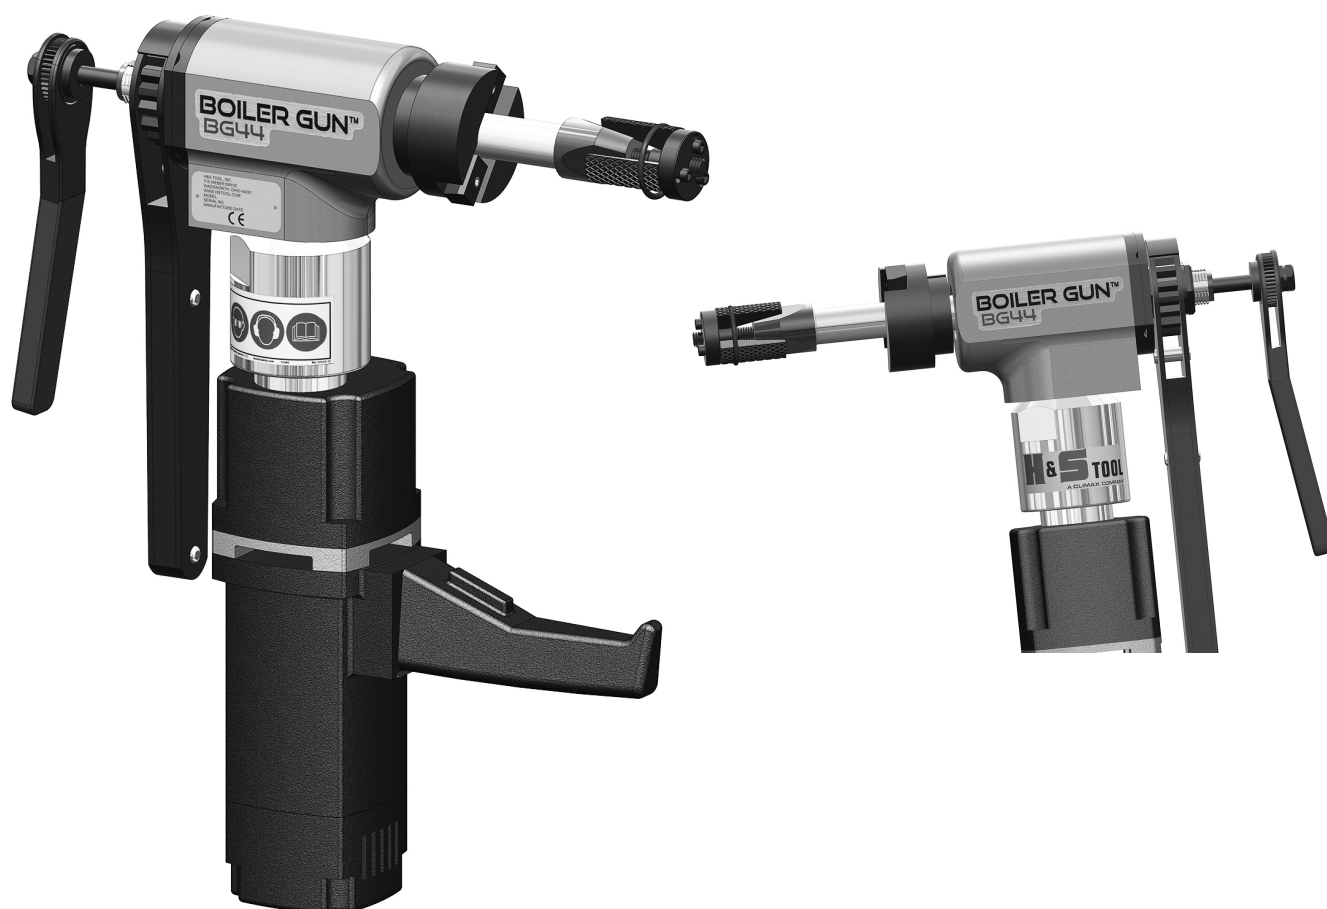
EMBLACEMENT DES ÉTIQUETTES SUR LA BG44 BOILER GUN
